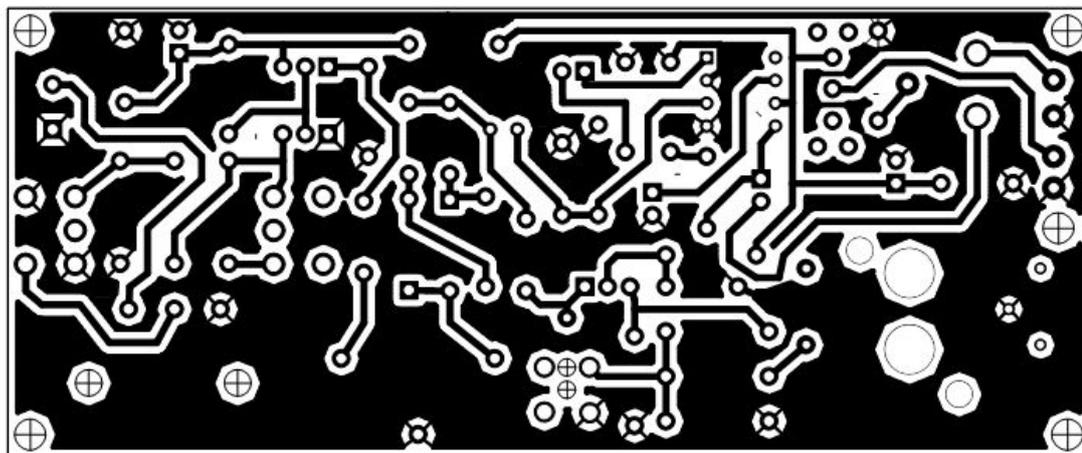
Печатная плата приемника. Вид со стороны деталей.
